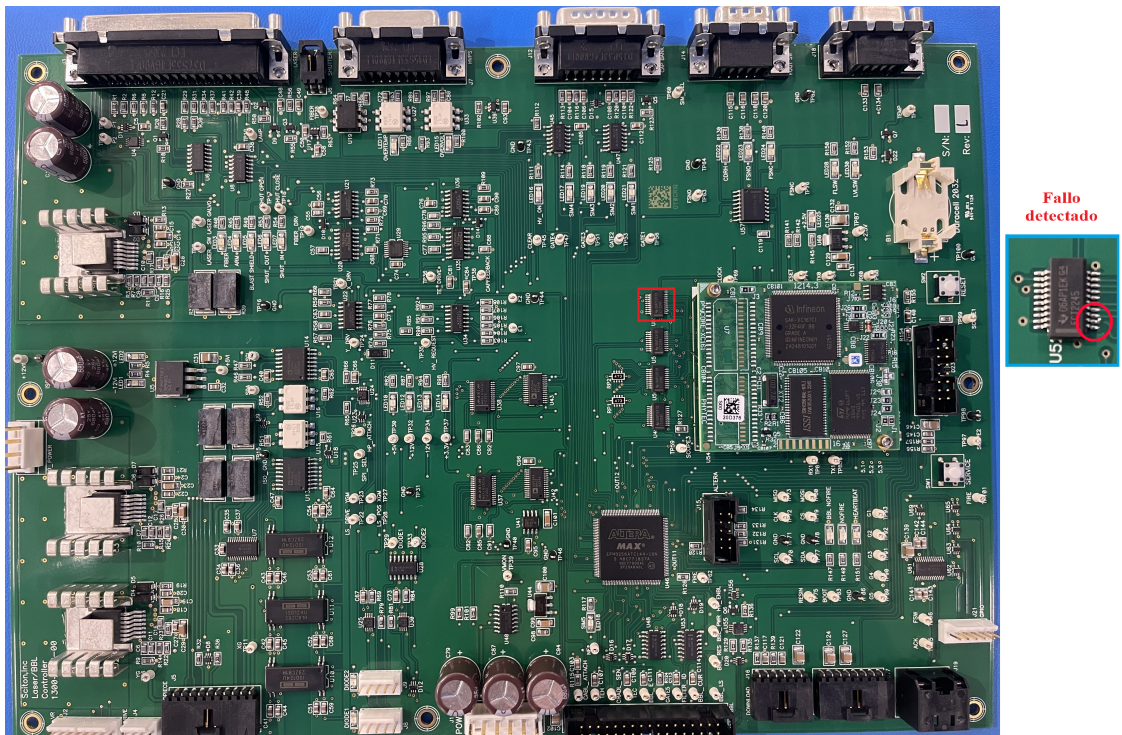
PCB 98 L con anomalía por soldadura detectada.
